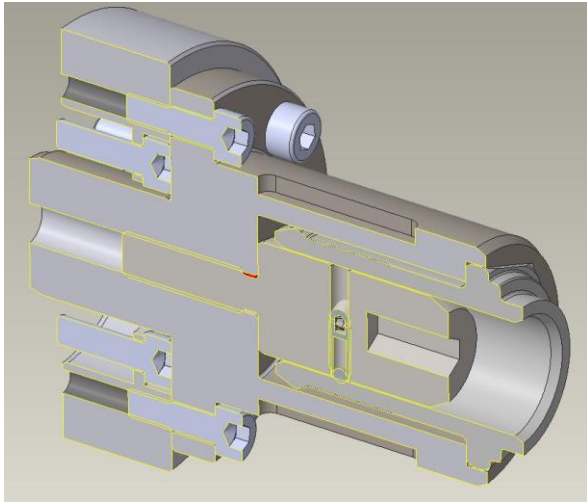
Konzept Werkstückaufnahme Reibschweißen
